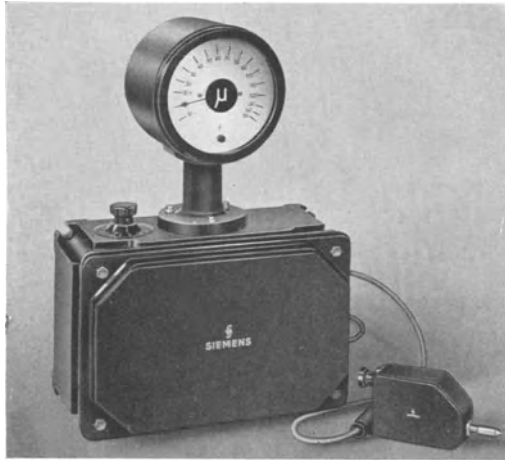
Bolometrische Meßlehre mit Schaltkasten für Steuerungen.
